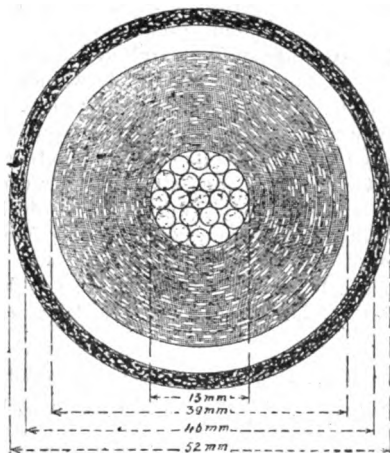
Coupe du câble Dessau-Bitterfeld à 60000 volts des Siemens-Schuckertwerke.
